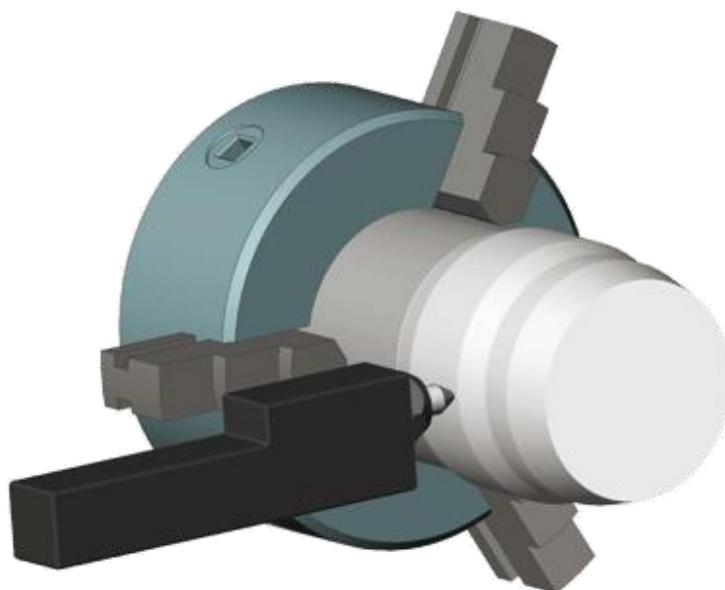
3D модель обработки детали на токарном станке с ЧПУ инструментом DB-3 Cogsidill Tool
